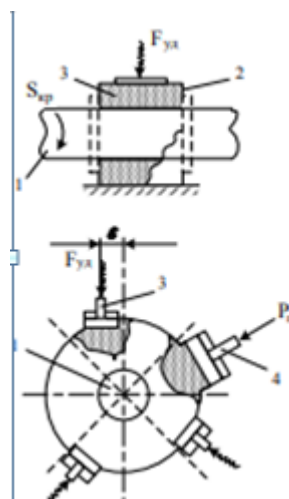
Схема многоконтактного виброударного упрочнителя [5]
